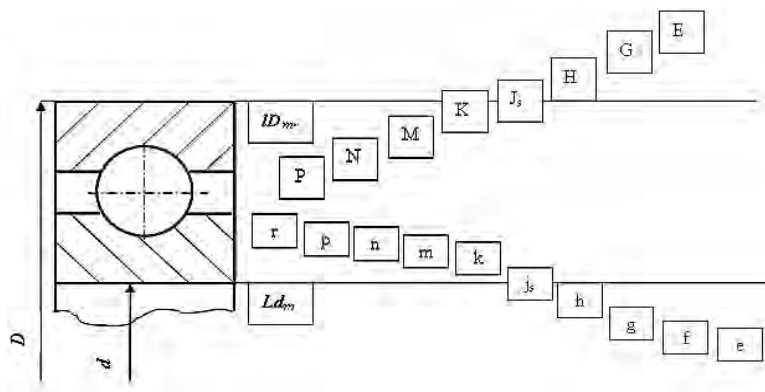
Схемы расположения полей допусков при посадках подшипников
